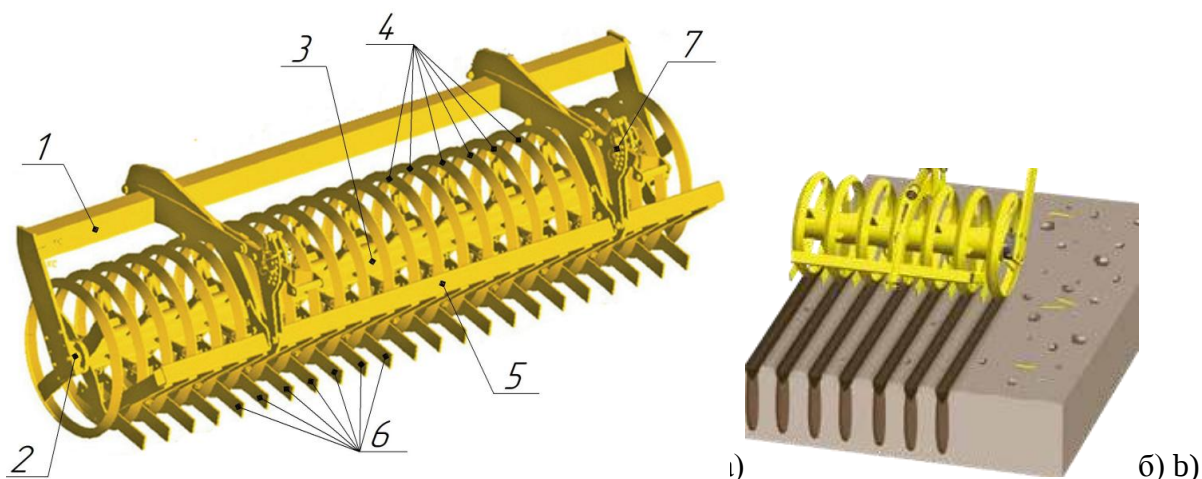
Общее устройство режуще-кольцевого катка с V-профилем колец дисковой бороны Terradisc (а) и схема его воздействия на почву (б):
